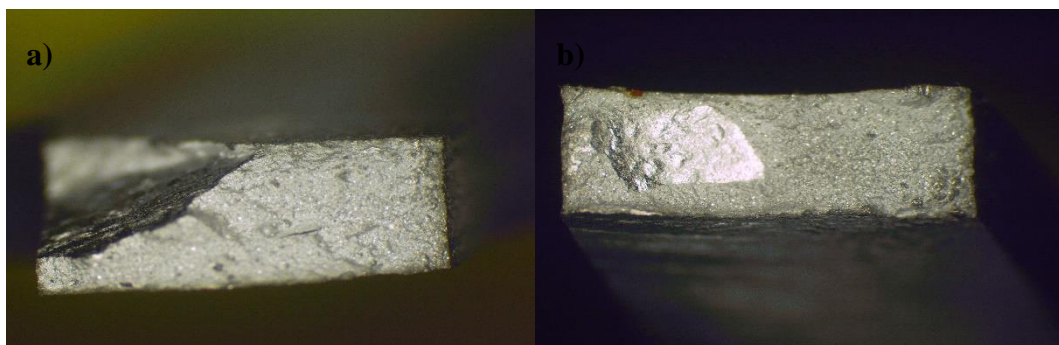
Superfícies de fratura dos provetes 5B (a) e 5C (b)
